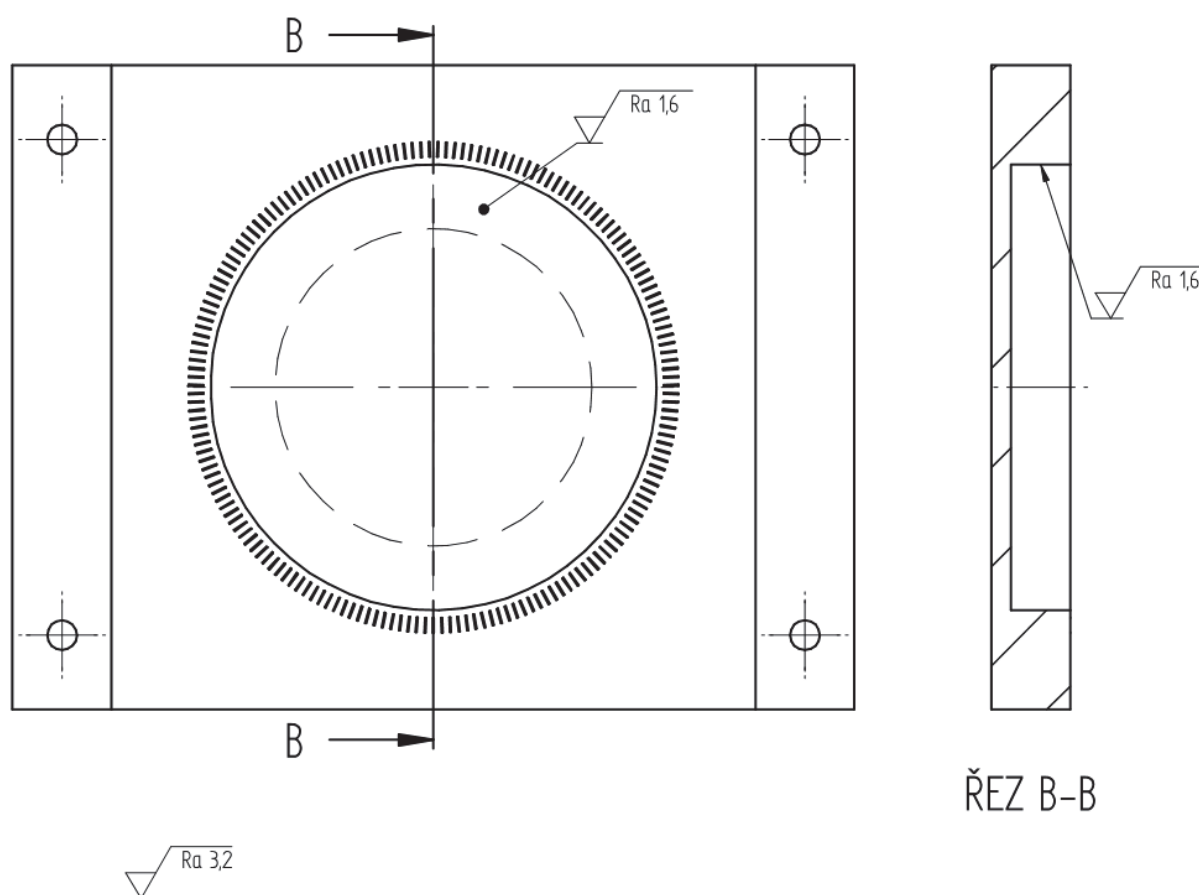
Kombinace tolerancí pro součást "otočný stůl"
